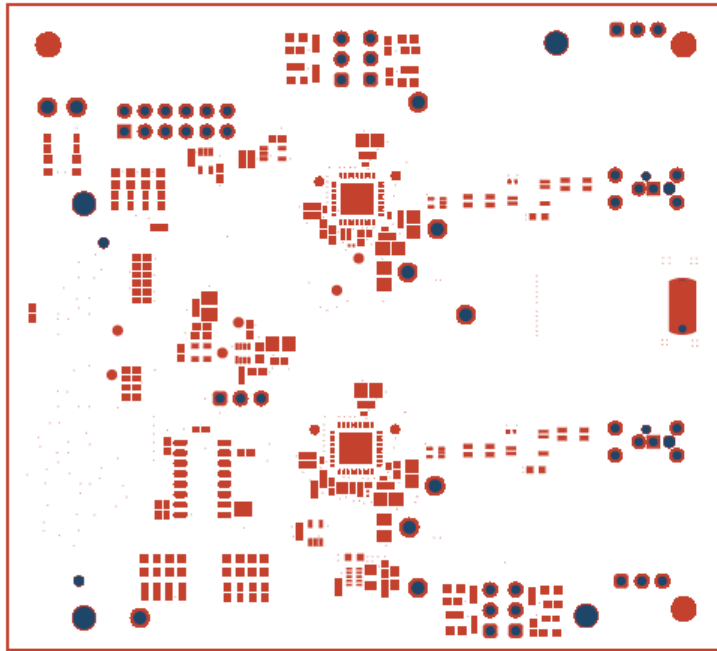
至图 3-18 展示了使用铜厚度为 2oz 的六层 PCB 的 DP83TG720-IND-SPE EVM 设计。
